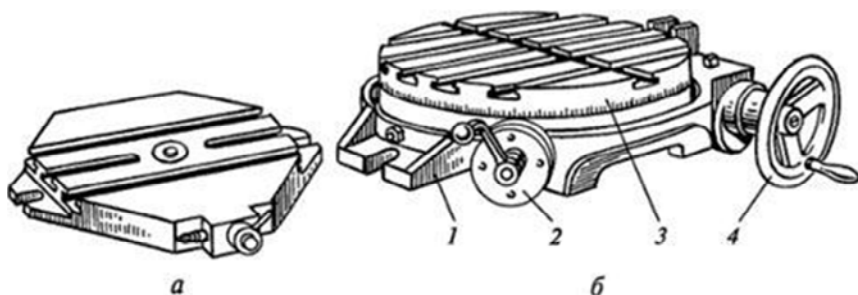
Столы: *а* – неповоротный; *б* – поворотный: *1* – кронштейн для крепления стола на станке; *2* – стопор; *3* – шкала отсчета угла поворота; *4* – рукоятка ручного поворота
